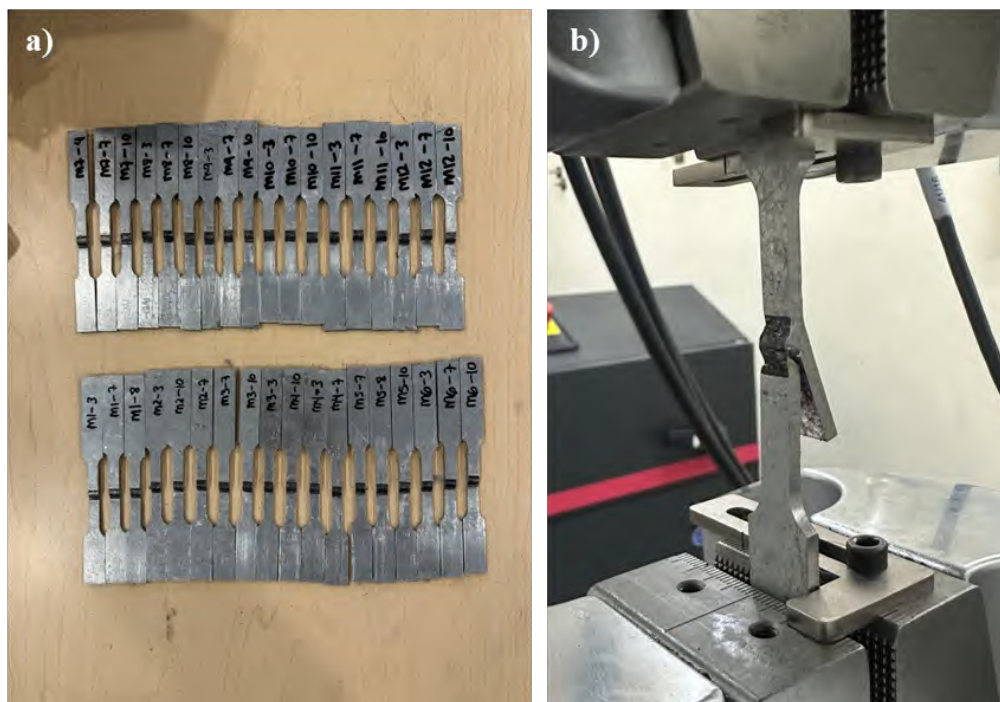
(a) Probetas de tracción extraídas de las uniones soldadas, (b) Probeta montada en la máquina universal durante el ensayo de tracción uniaxial.
